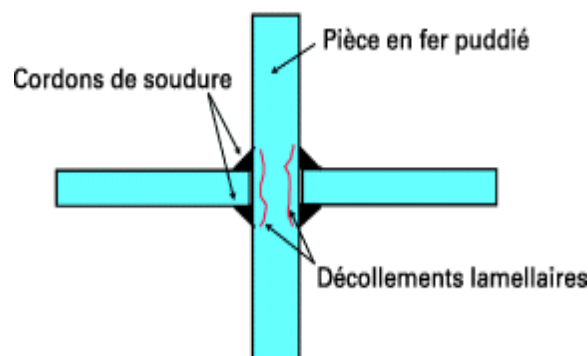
Exemple de soudure réalisée sur une pièce métallique en fer puddlé [9]
